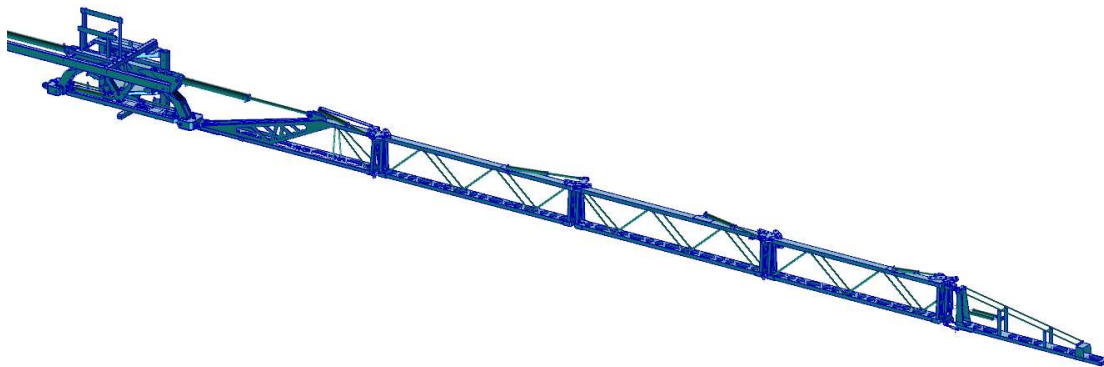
Modelo de la estructura del pulverizador de barras facilitado por el fabricante
